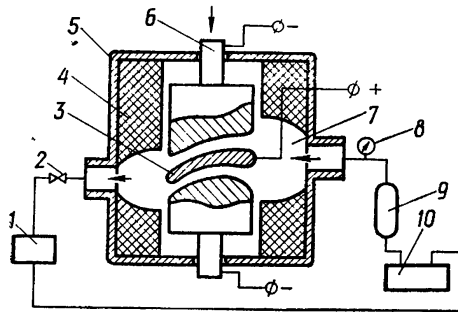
Схема обробки лопатки рухомими електродами
